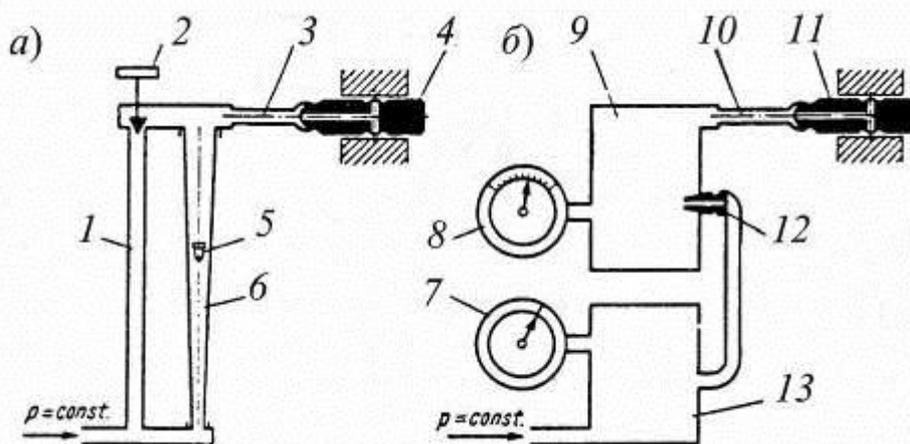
Пневматические приборы для измерения диаметров и длин: а — на базе ротаметра; б — на базе пружинного манометра; 1 — обводной канал; 2 — кран; 3 — резиновая трубка; 4, 11 — пневматический калибр; 5 — поплавок; 6 — трубка ротаметра; 7,8 — манометры; 9 — выходная камера; 10 — резиновый шланг; 12 — входное сопло; 13 — входная камера
